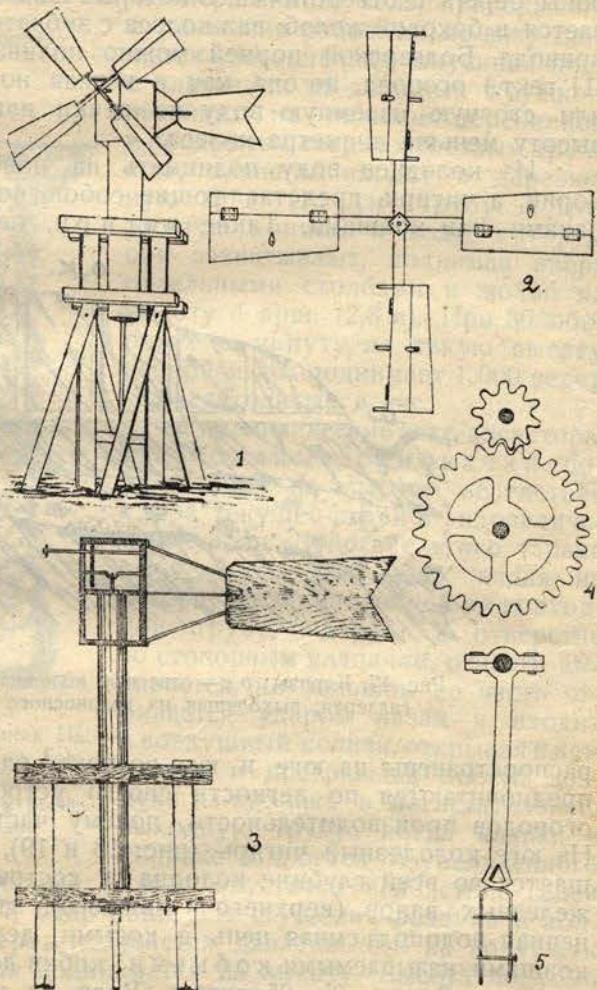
Ветряк Бессарабова: 1) общий вид; 2) крылья с складнями на петлях; 3) коробка с рулем и с двумя осями, держащейся на деревянной трубе; 4) зубчатая передача; 5) штанга с соединением для кривого колена и штанги насоса.
